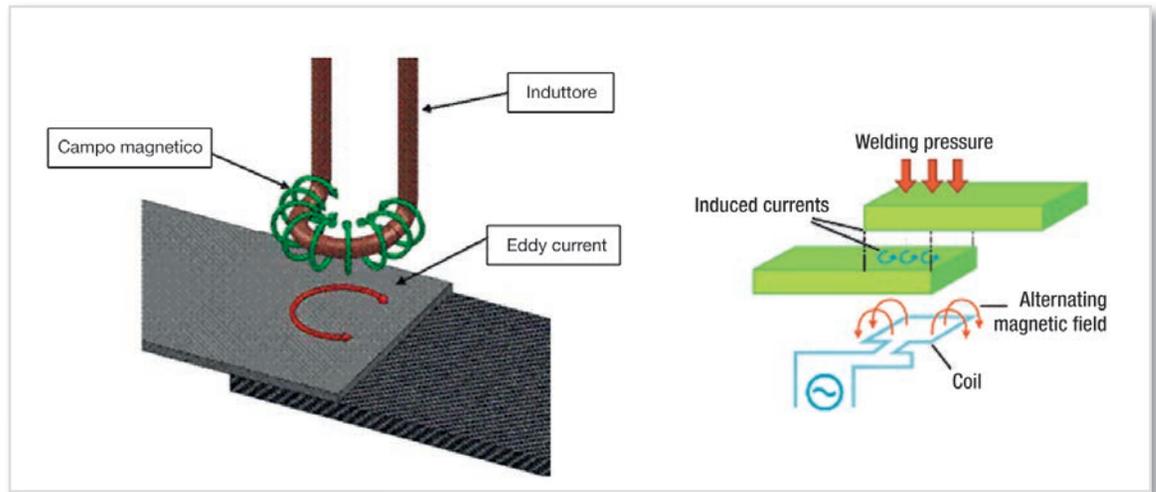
Induction Welding Saldatura ad induzione elettromagnetica
